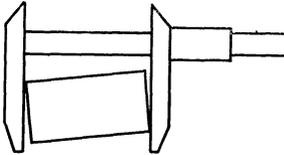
Meßfehler durch Verkanten des Meßwerkzeuges.
